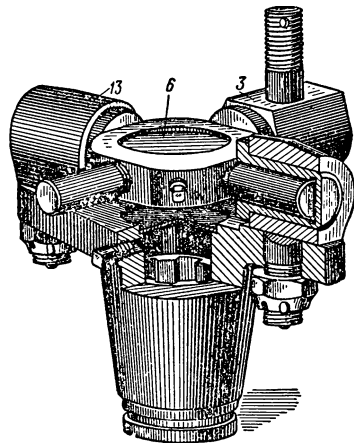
Общий вид карданного соединения (обозначения см. на рис. 163)
